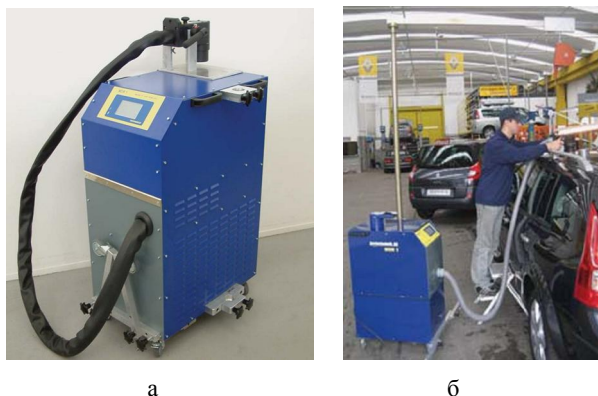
Магнитное приспособление для удаления вмятин концерна "Beulentechnik AG": а – источник мощности с инструментом; б – приспособление в действии
